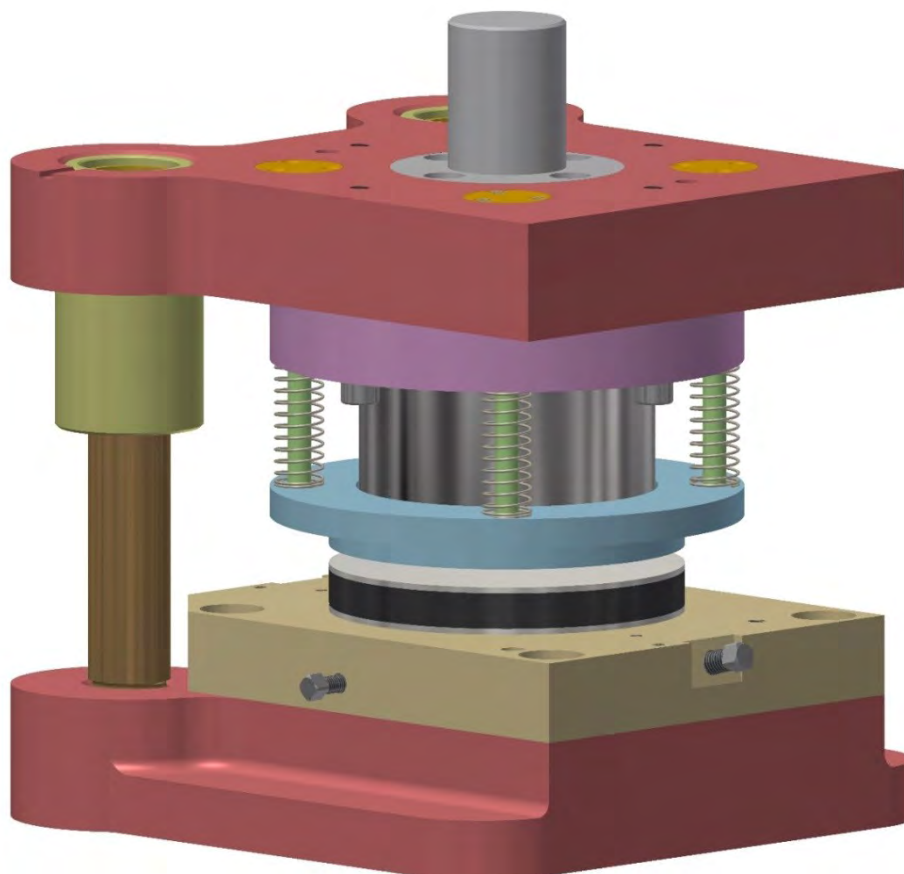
Трехмерная модель блок-штампа для изготовления прокладочных деталей разделительными операциями с металлическими слоями и слоями из эластичного композитного материала.
